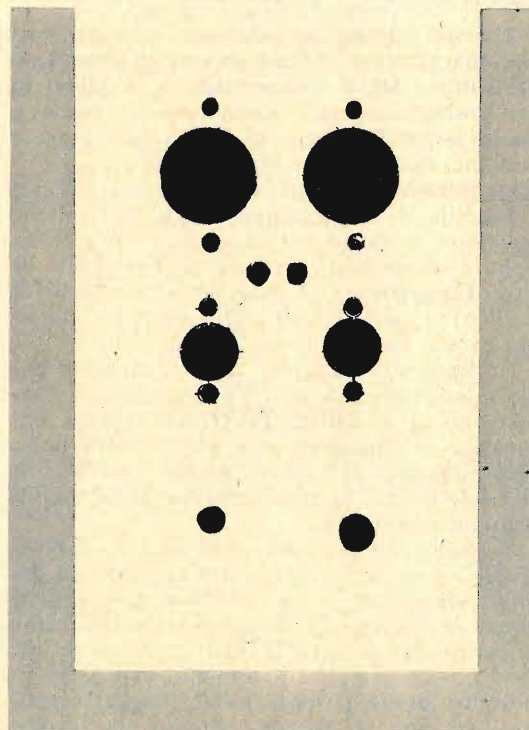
Schema pratico di montaggio di componenti sul pannello frontale.
